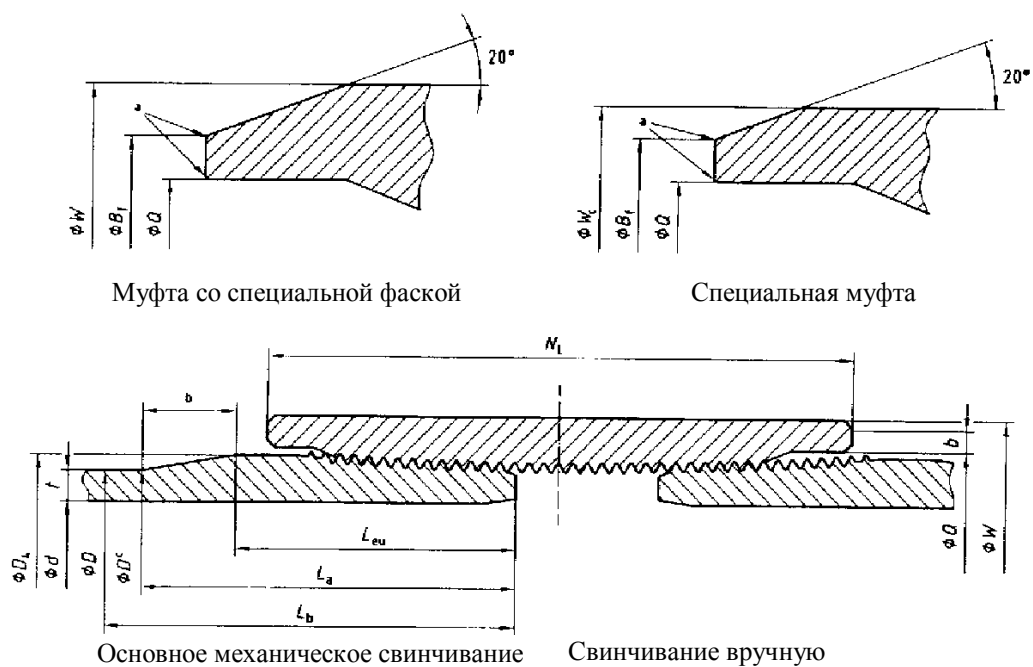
Обсадные трубы и муфта с упорной резьбой
